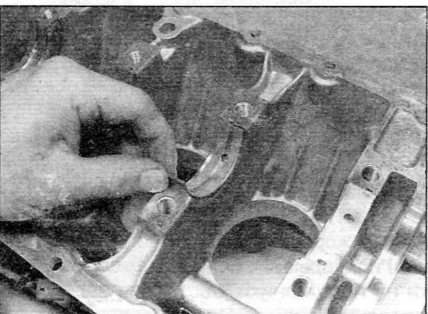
Установите канавчатые вкладыши для подшипников № 2 и 4 (двигатели 1.4 л)
